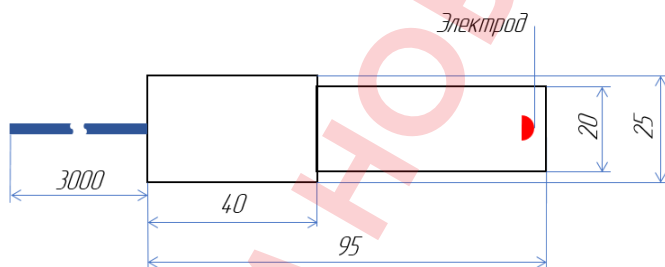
Пример установки скиммерного датчика с креплением типа "профиль"
